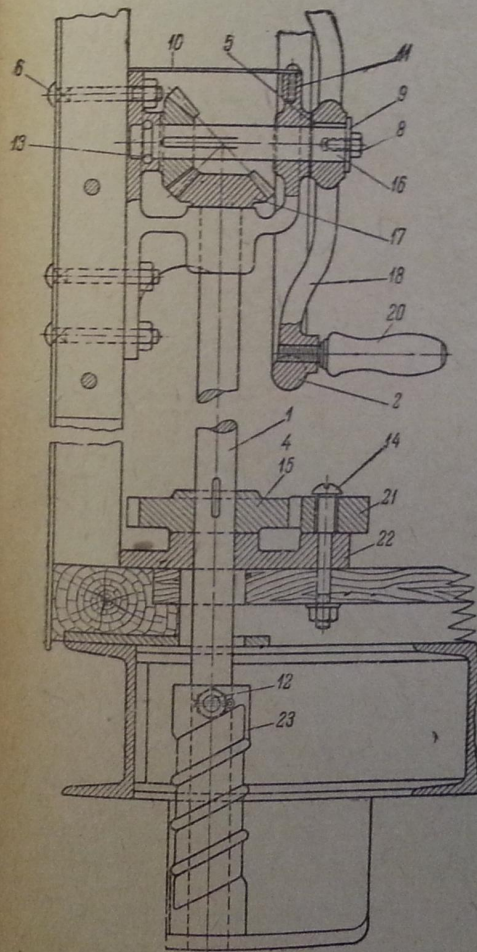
Ручной привод тормоза прицепного вагона на свободных осях.
